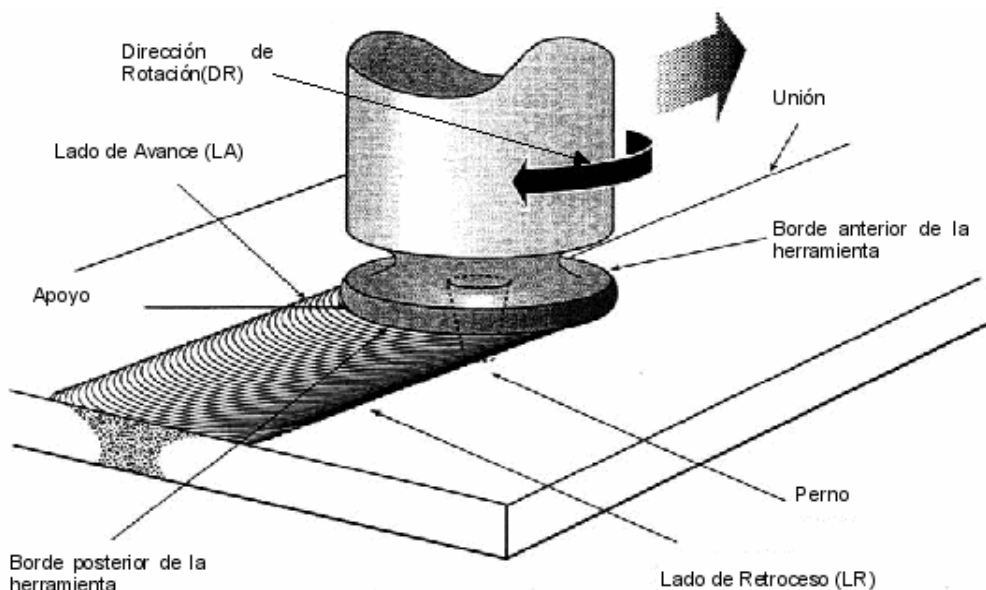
Esquema del proceso de Soldadura por Fricción-Agitación
